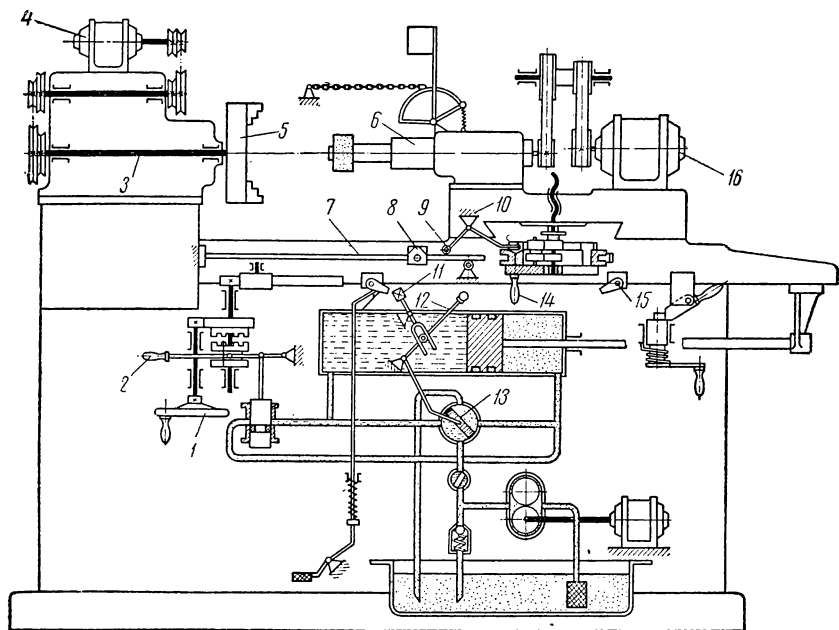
Гидрокинематическая схема внутришлифовального станка 3250
